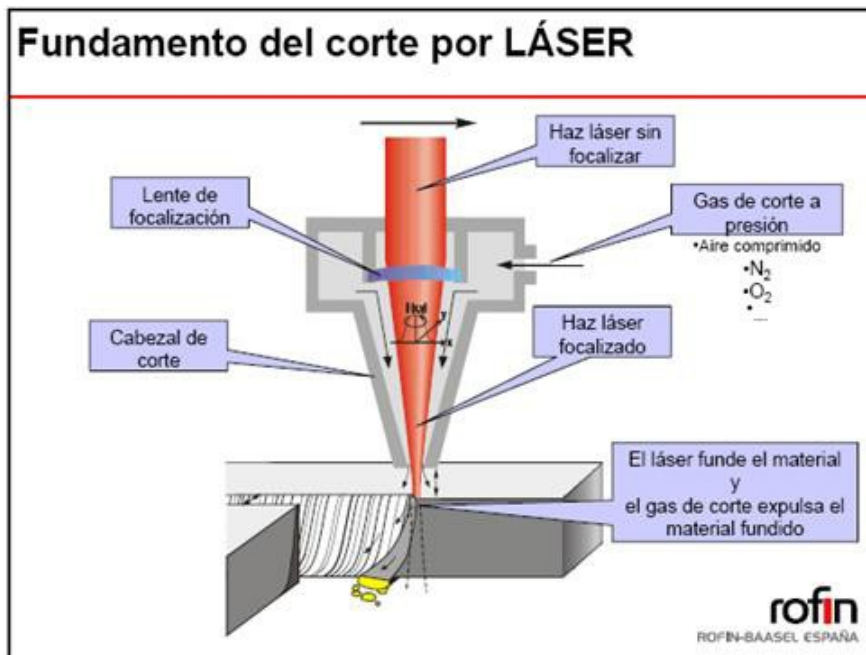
b) Fundamentos del corte por láser. [S-28]
